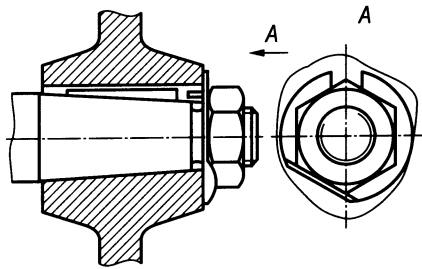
Крепление гайкой и отгибной шайбой с лапкой
